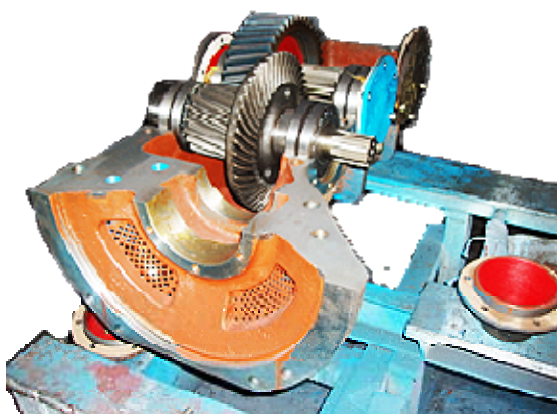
Загальний вигляд редуктора шахтного конвеєра
